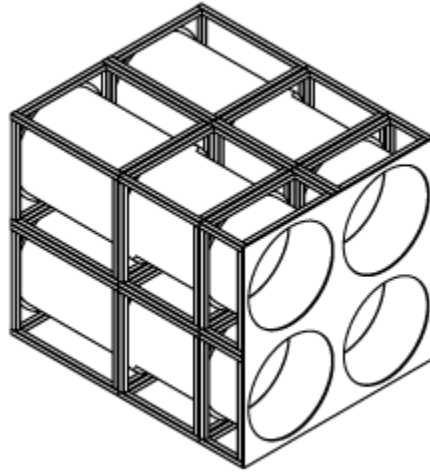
Detalle constructivo de la plana de potencia. Fuente: Generación propia (SolidWorks 2018)
